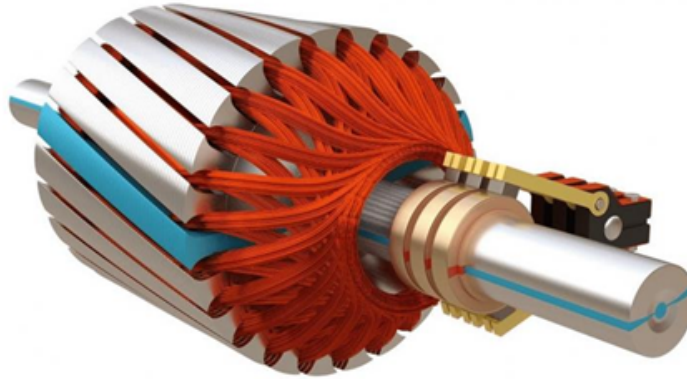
Moteur asynchrone à rotor bobiné [7]
